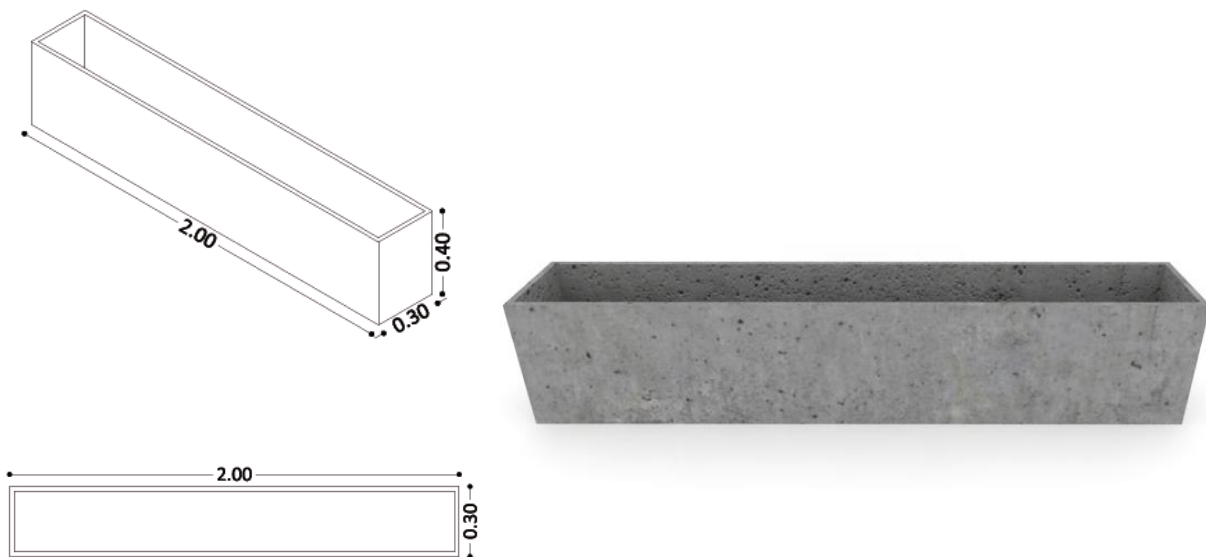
Planimetría y render, jardinera 2. Fuente: grupo de investigación.
